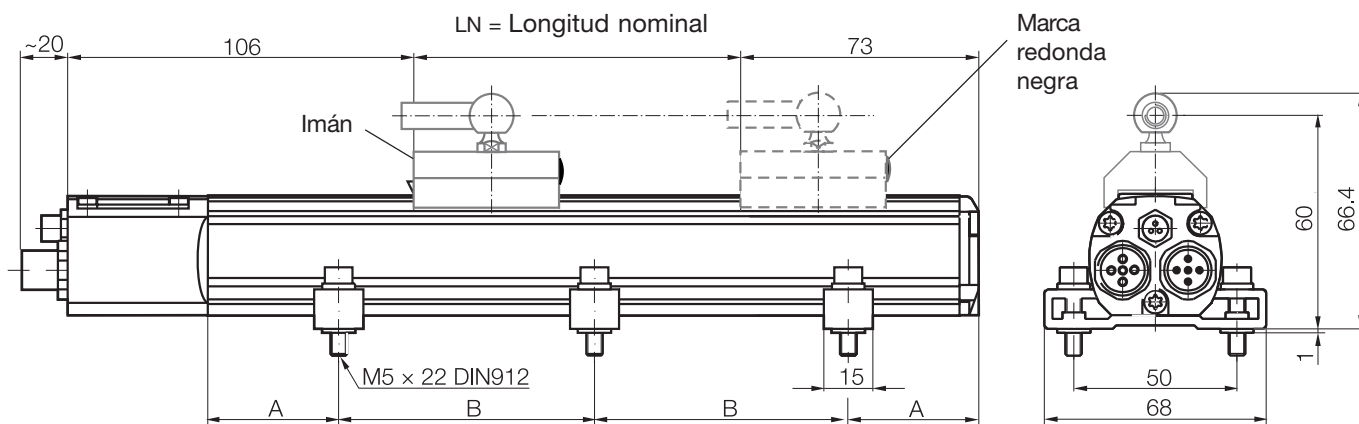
Dibujo acotado (transductor de desplazamiento lineal BTL5...P-S103 con sensor de posición guiado BTL5-F-2814-1S)
